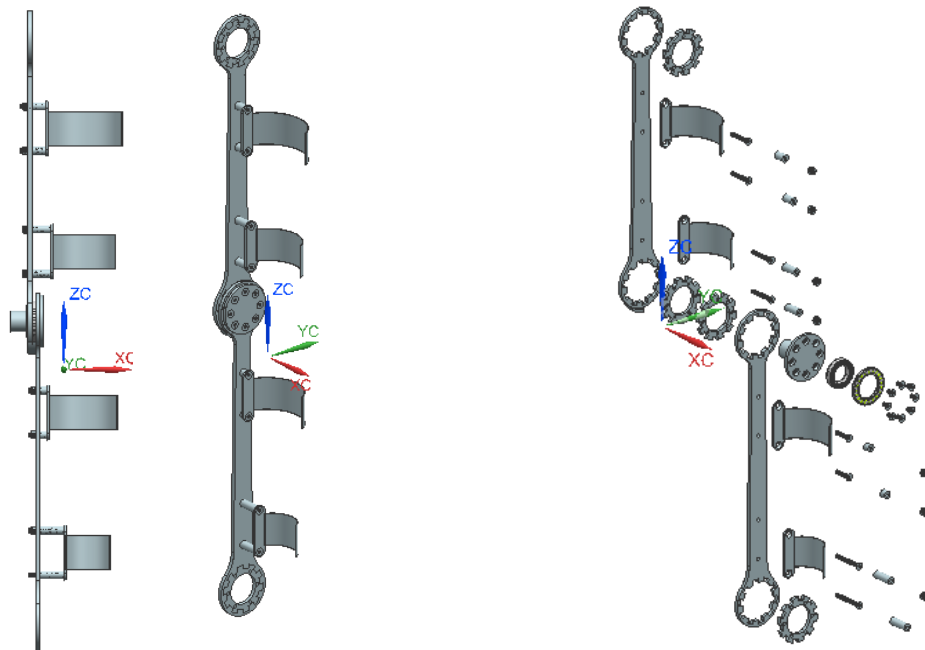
Ensamble y explosivo de la pierna derecha.
